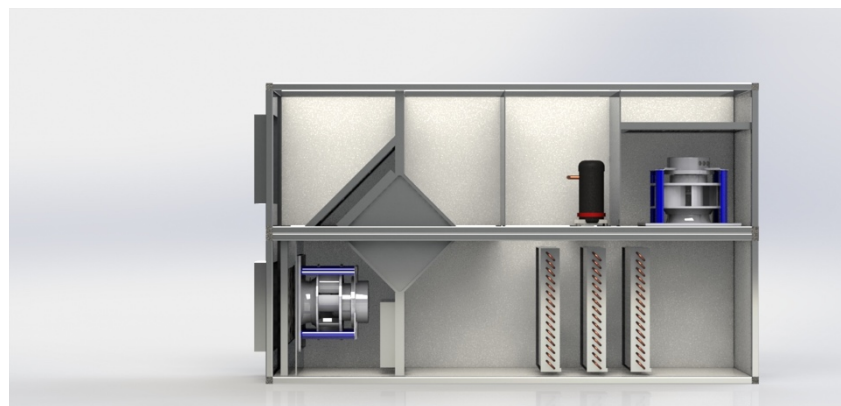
Diseño en detalle de la máquina utilizando SolidWorks
